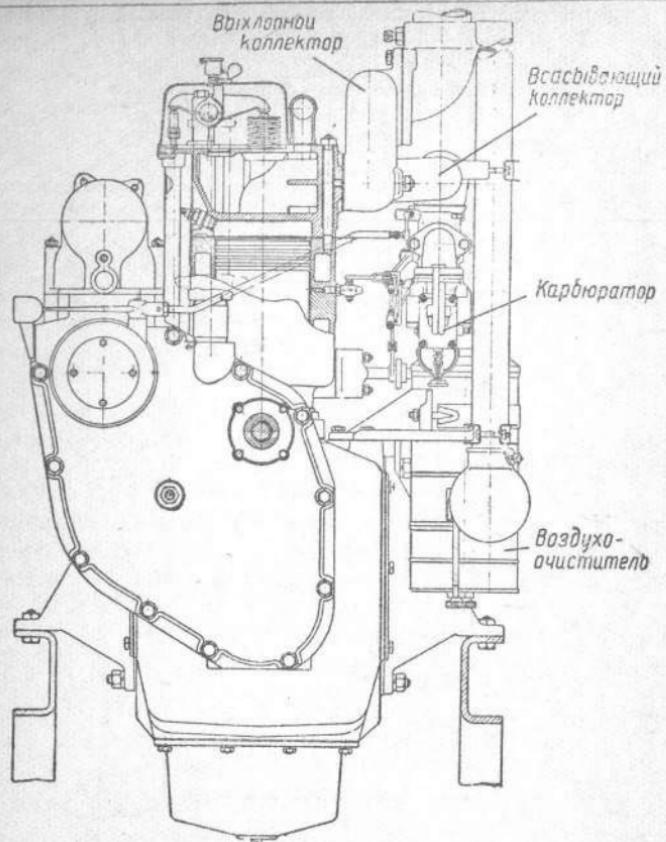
Газовый двигатель трактора «сталинец-60» (вид спереди)
